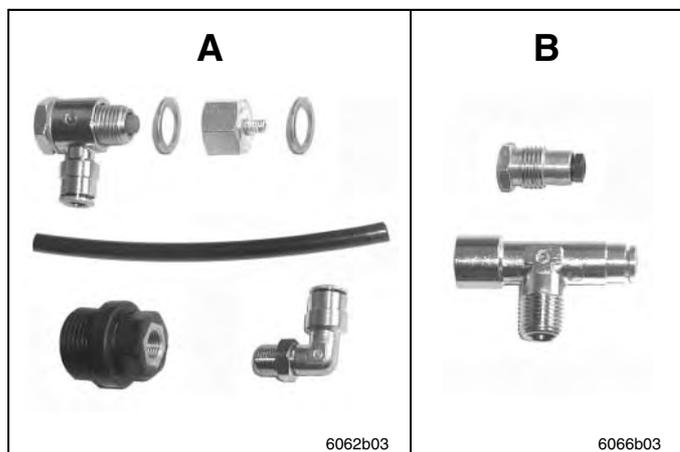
Nachrüstset: Druckbegrenzungsventil mit Fettrückführung zum Behälter
